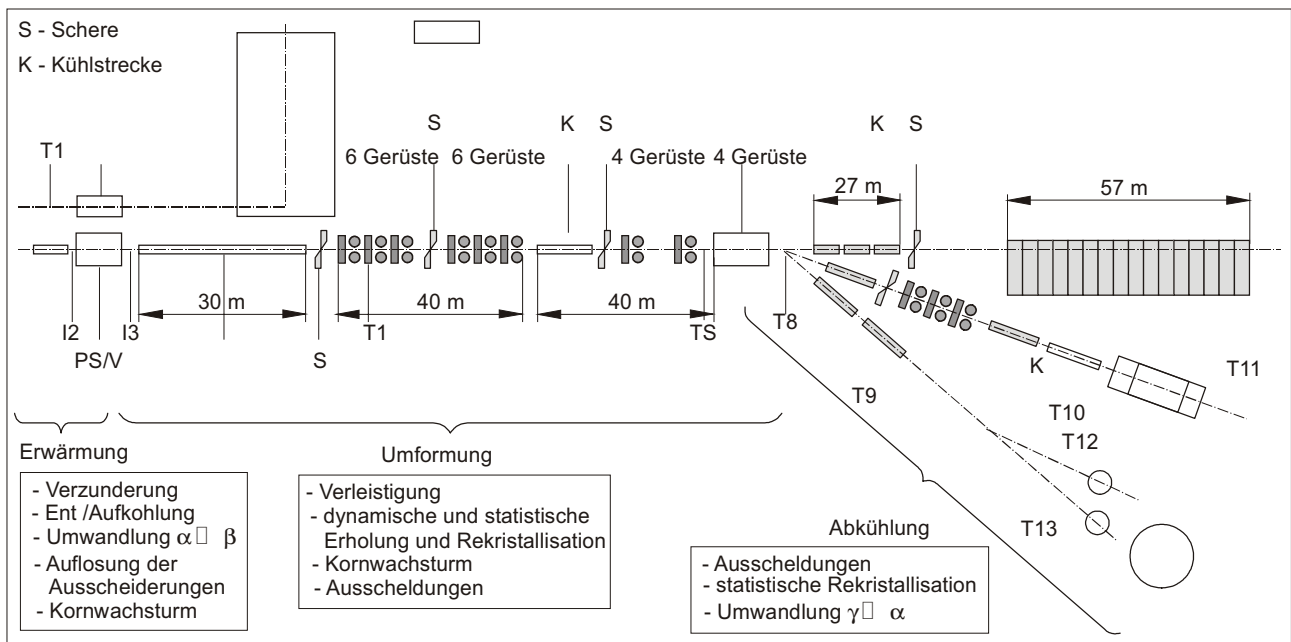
Layout einer kombinierten Stabstahl- und Drahtstraße [9]
